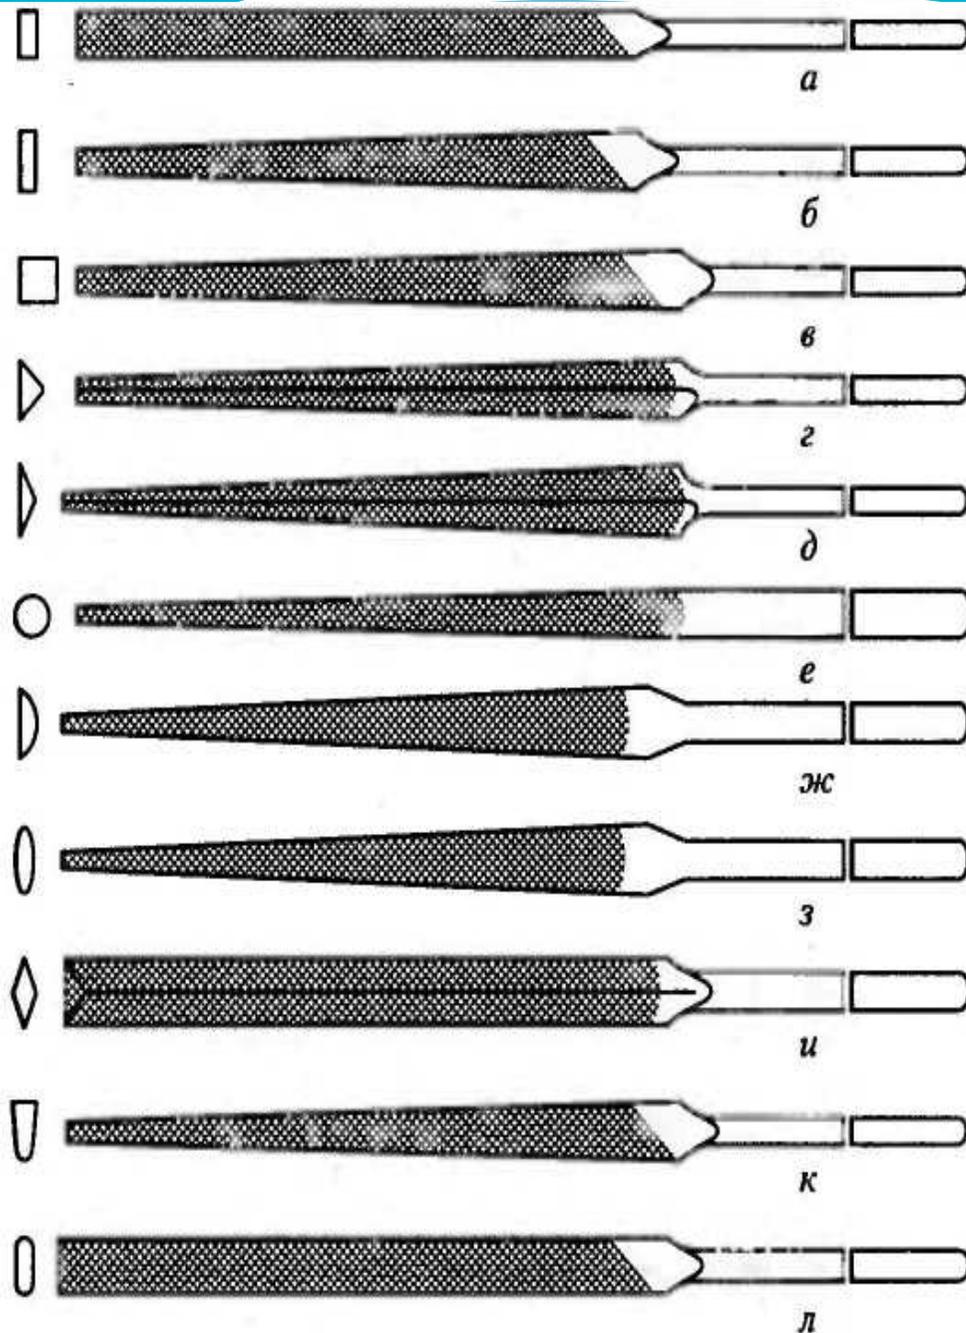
Надфили: а, б - плоские; в — квадратный; г, д — трехгранные; е — круглый; ж — полукруглый; з — оливообразный; и - ромбический; к - трапецеидальный; л - галтельный
